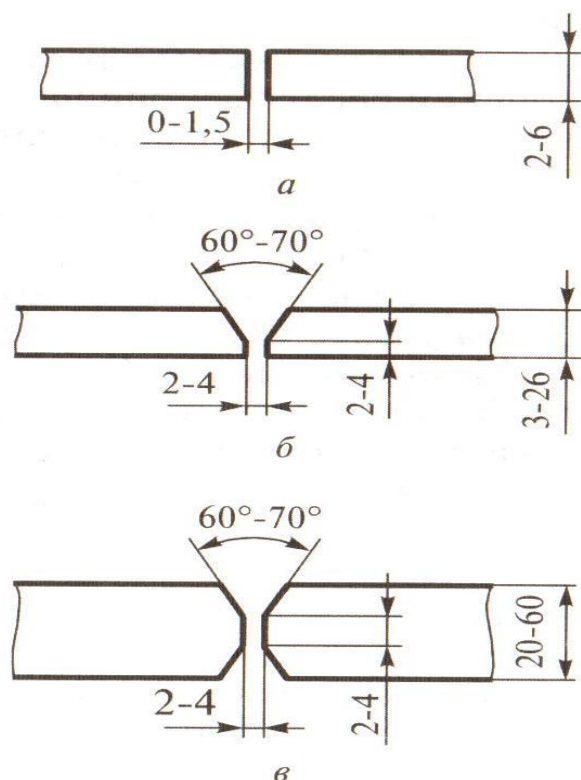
Способы подготовки кромок для стыковых соединений при дуговой электросварке:
